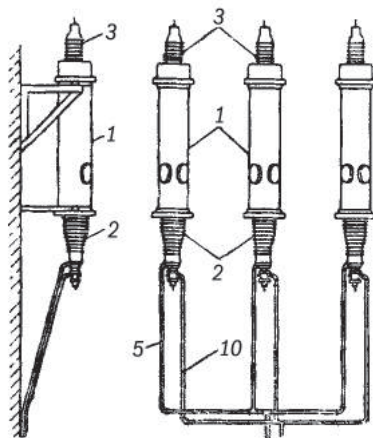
4 Трехфазовый масляный выключатель горшкового типа на 100 кв (1908 г.)
